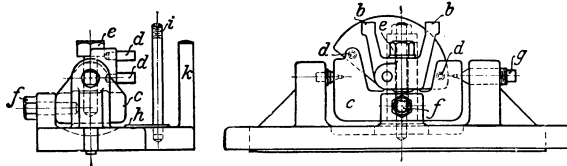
Um 90° schwenkbare Fräsvorrichtung für Konsole.
